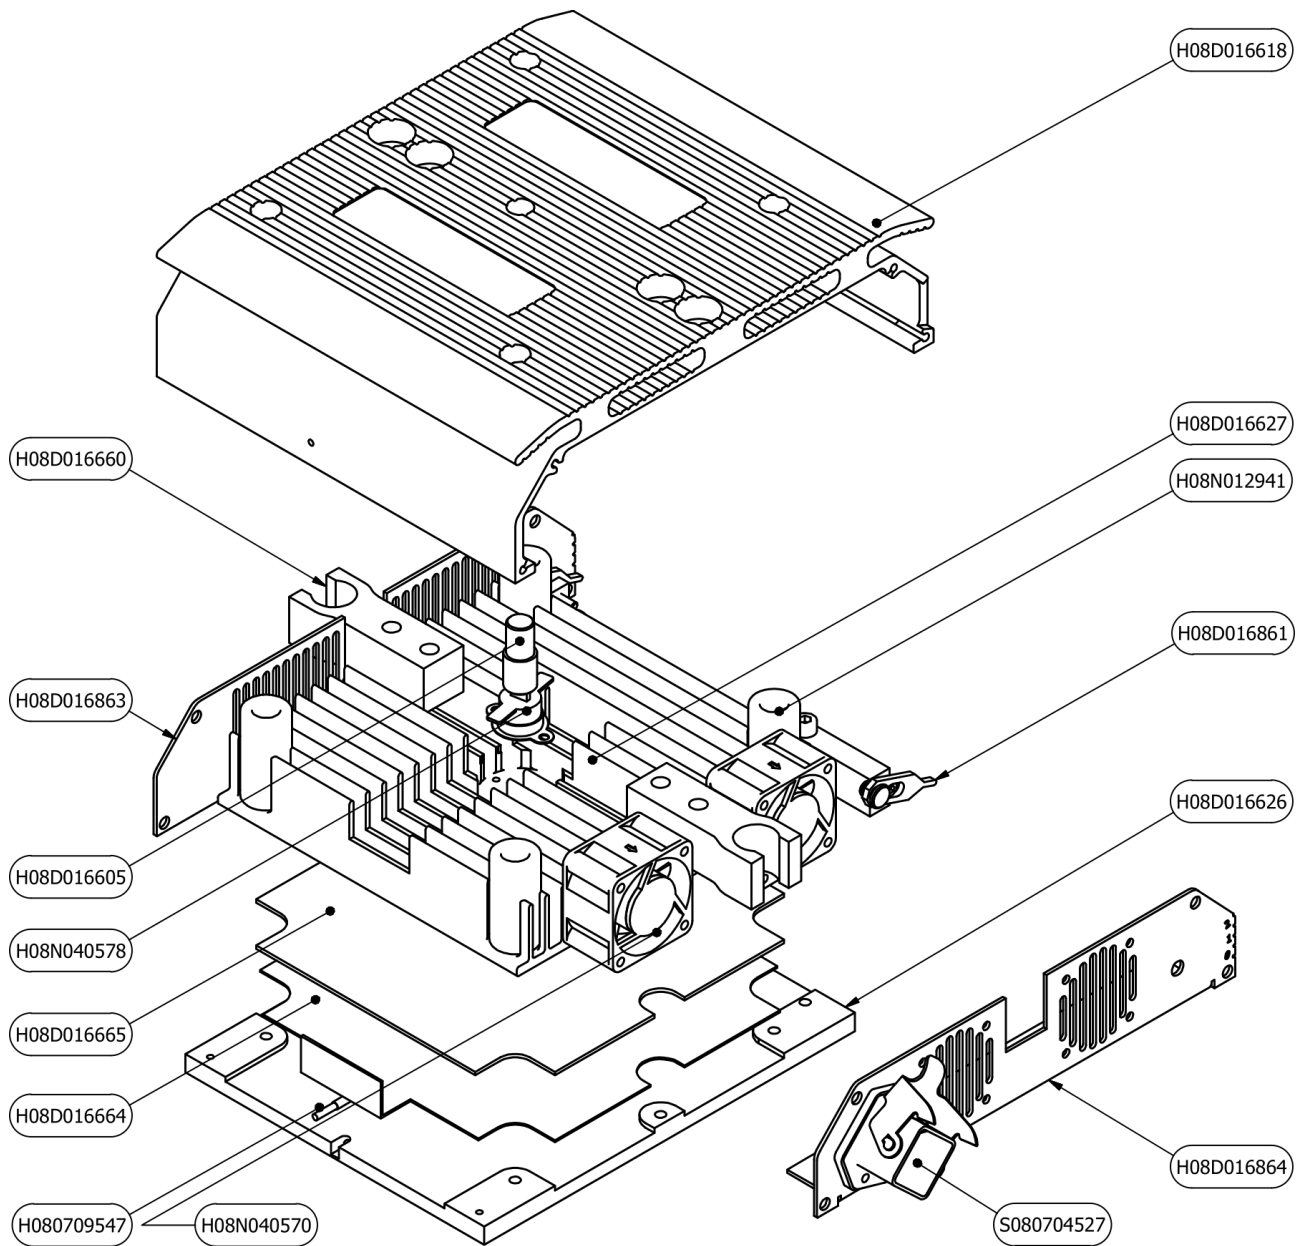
H08D016625 Unidad de placa de calentamiento superior PML-100
